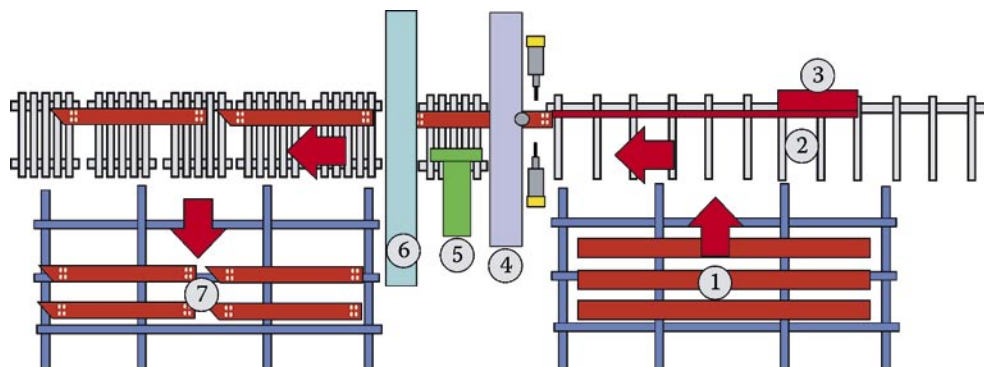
Линия сверловки, маркировки и мерной порезки профильного проката:
